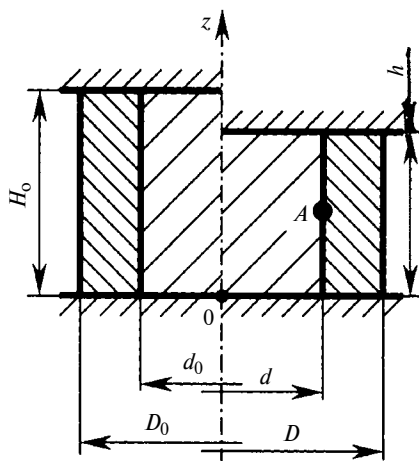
Схема осадки цилиндрического сердечника в оболочке
